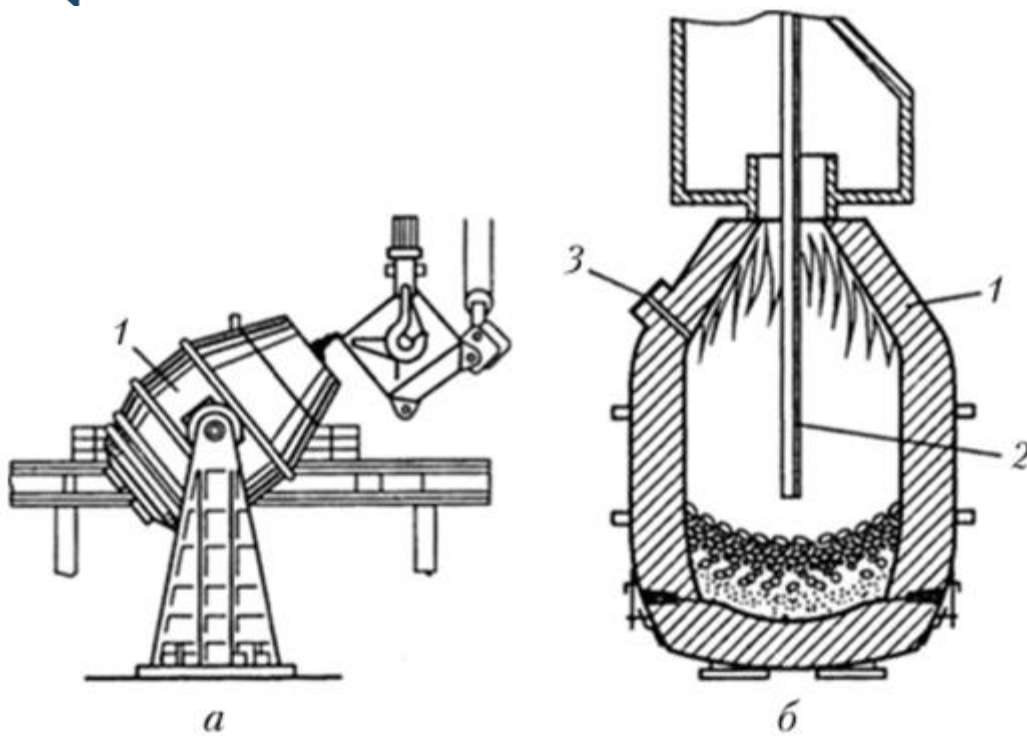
Кисневий конвертер: а - заливка чавуну; б - продування киснем; 1 - корпус конвертера; 2 - водоохолоджувана фурма для подачі кисню; 3 - вихідний отвір для сталі [5]
